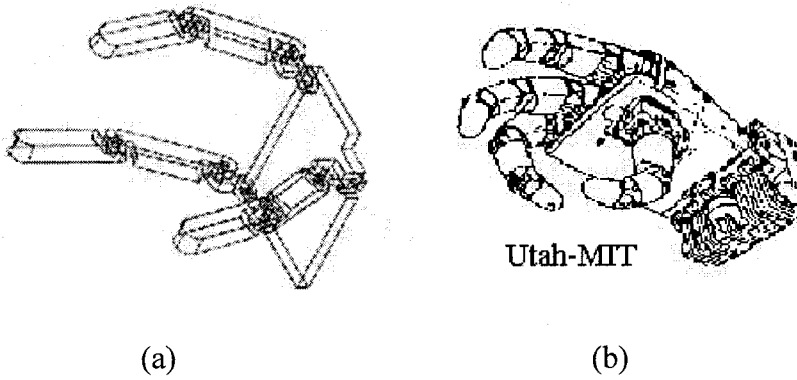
Stanford/JPL Robot Elde Makara-ip mekanizması [30]
